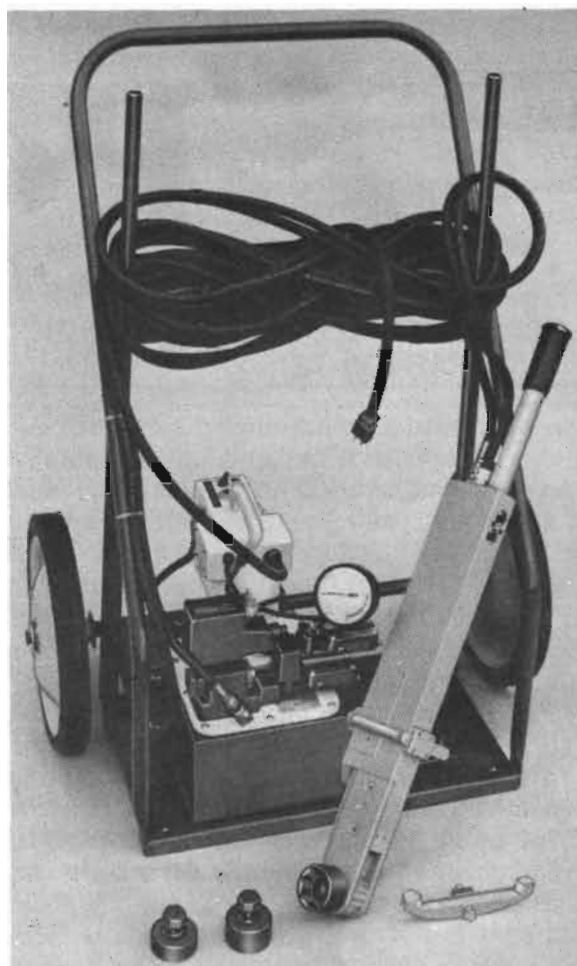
Llave para tuercas de cojinetes principales 9523800
